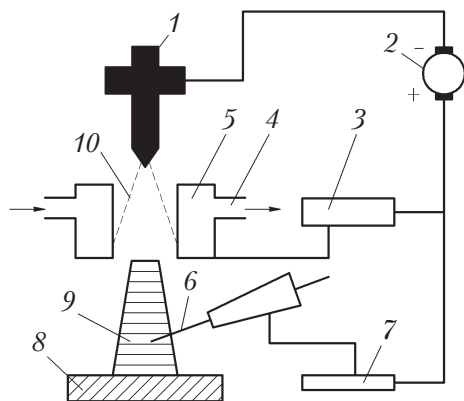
Схема плазменного напыления проволочными (прутковыми) материалами:
